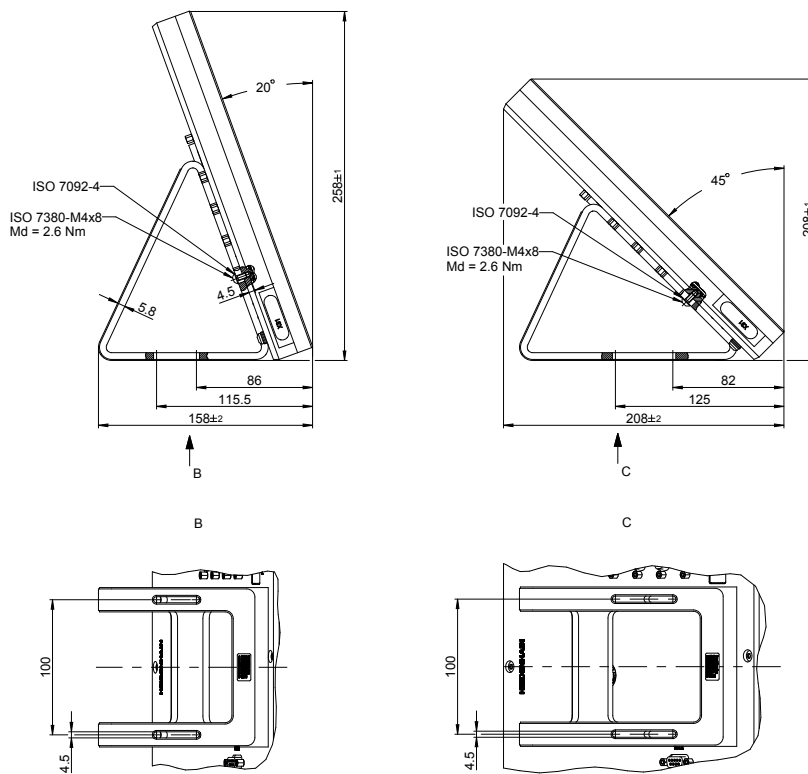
Dimensões do aparelho com pé de suporte Duo-Pos
